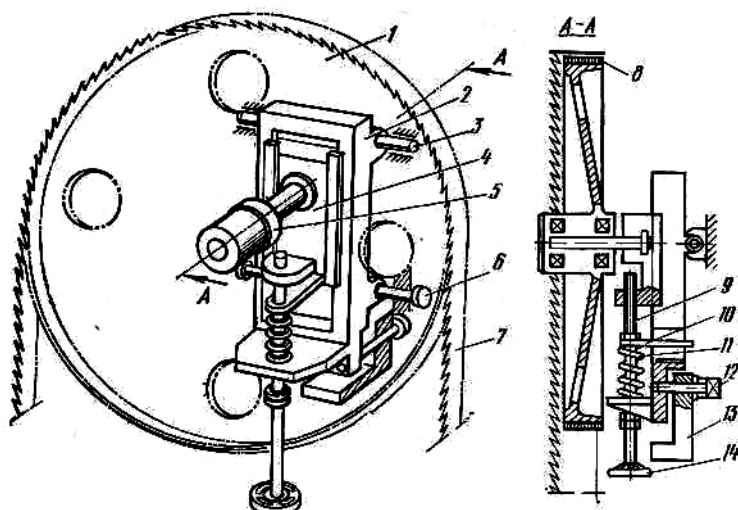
Направляющее устройство ленточнопильного станка: 1 — шкив, 2 — кронштейн, 3 — ось, 4 — ползун, 5 — ступица шкива, 6 — стопор, 7 — пила, 8 — бандаж, 9 — винт, 10 — рычаг, 11 — пружина, 12 — винт регулировки наклона шкива, 13 — станина, 14 — маховичок
